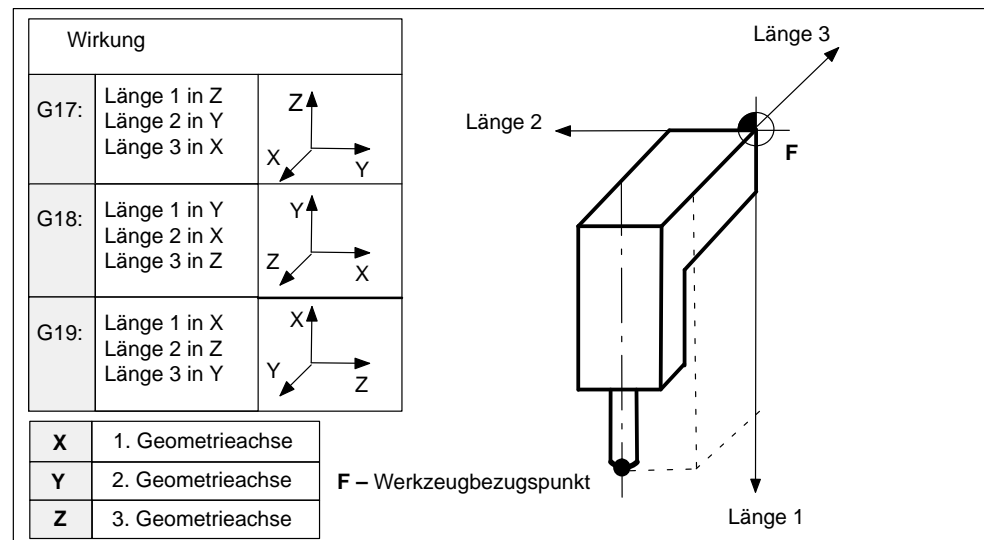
Wirkung der Werkzeuglängenkorrekturen dreidimensional
